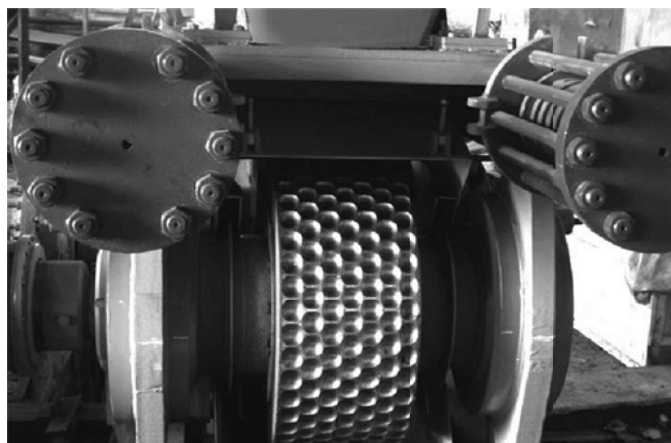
Внешний вид брикетировочного пресса ПБВ-700/400-200 производства ЗАО «СПАЙДЕРМАШ» с видом на рабочий валок
